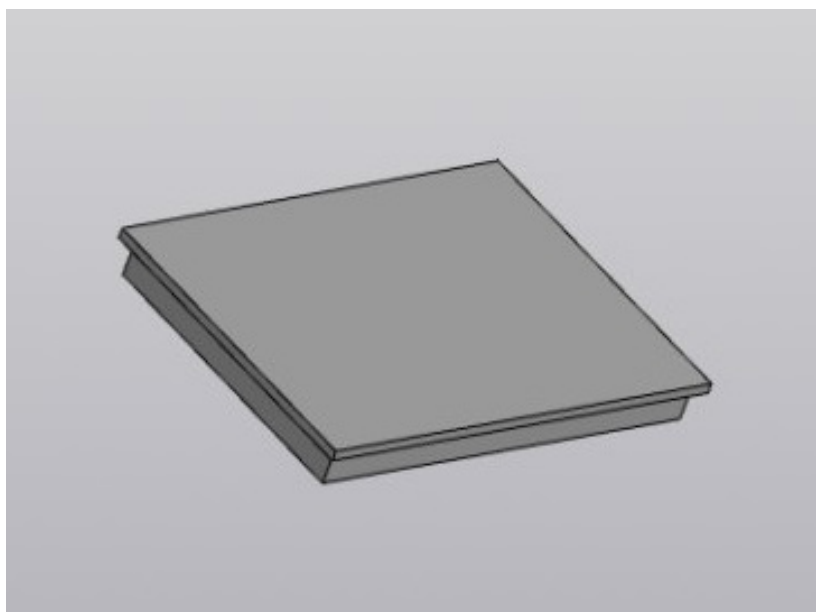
Задня частина корпусу пристрою, вигляд спереду.
